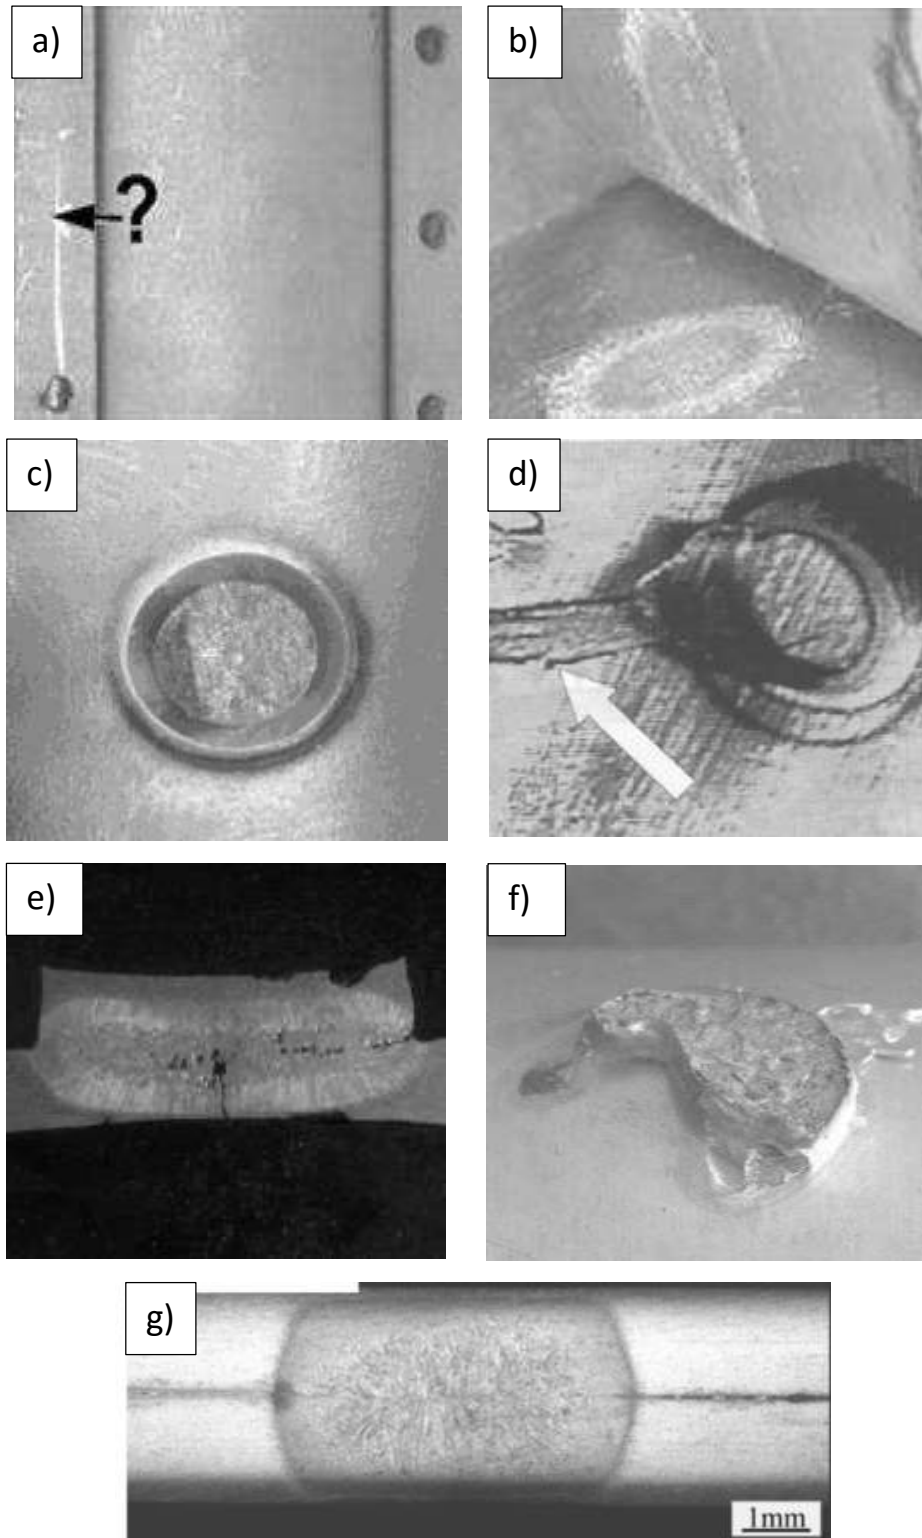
a) Falta de soldadura, b) soldadura atascada, c) indentación excesiva, d) expulsión e) grietas y agujeros/poros, f) soldaduras no circulares, g) soldadura de tamaño insuficiente [13].
